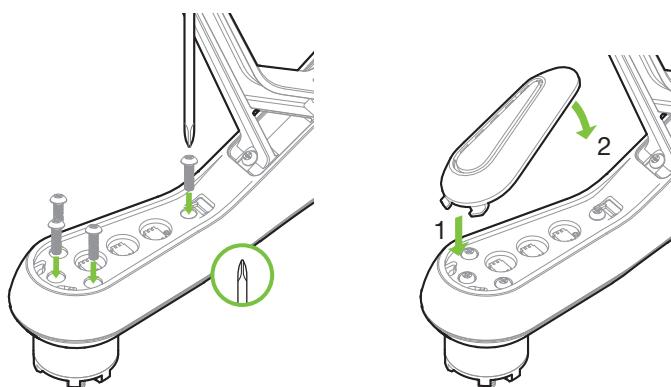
Fixation de fuseau-moteur et de couvercle de voyant
